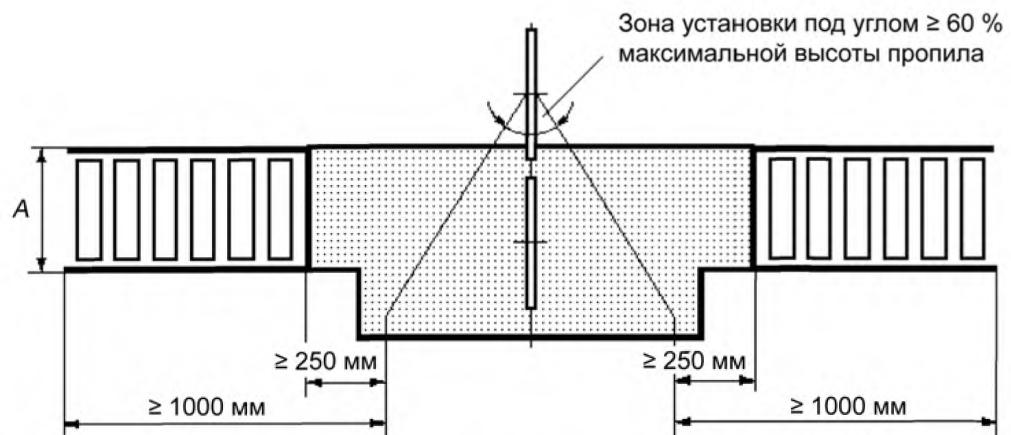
б) – Опорная поверхность для обрабатываемой заготовки в станках с ручным обслуживанием и в станках-полуавтоматах с диаметрами дисковой пилы > 315 мм
